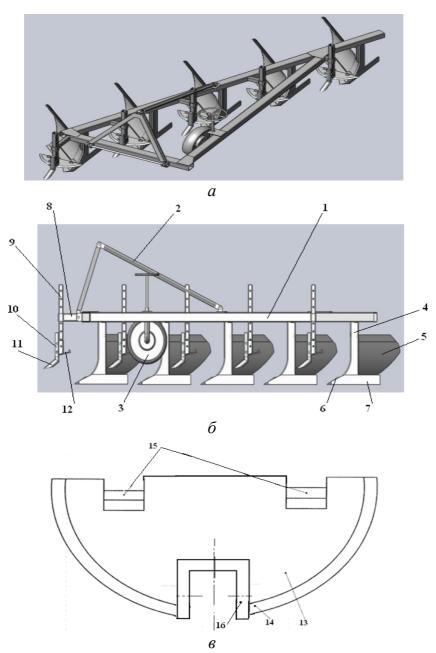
Схема предлагаемого универсального средства для обработки почвы: а — аксонометрия плуга; б — плуг вид сбоку; б — лапа вид сверху — повернуто (обозначения в тексте)
